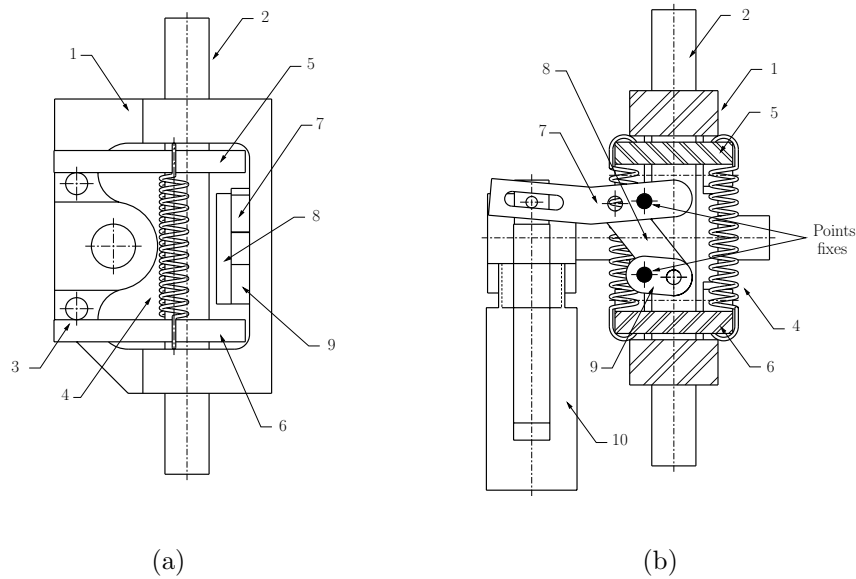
Mécanisme de blocage des pattes : (a) vue de face et (b) vue de droite.
